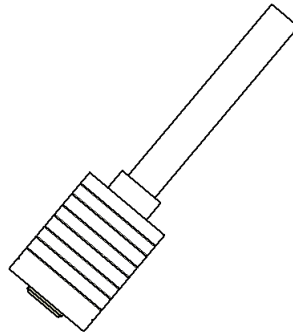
Ескіз пристосування для обробки циліндричних поверхонь
